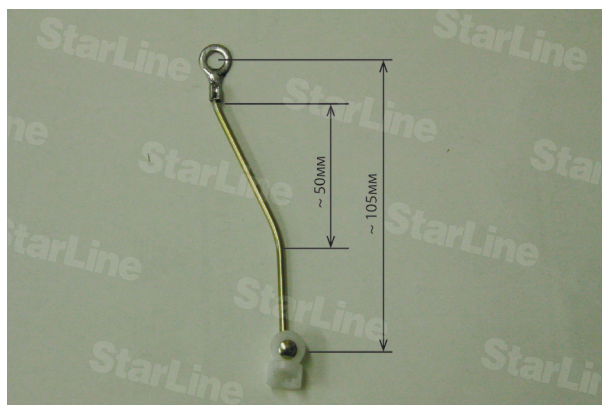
Тяга привода задней левой двери (вид сверху)
